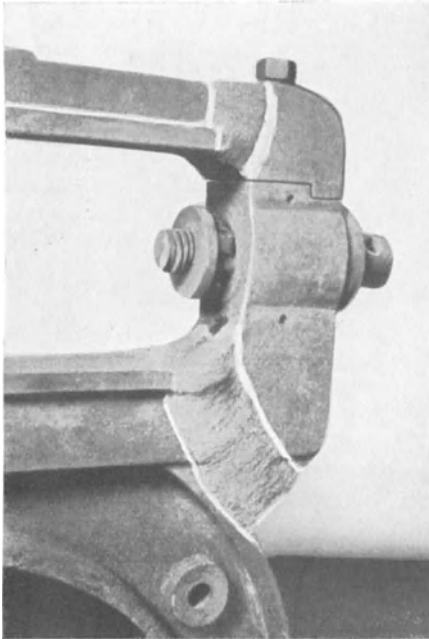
Schweißung am Ständer einer Gummiwalze.
